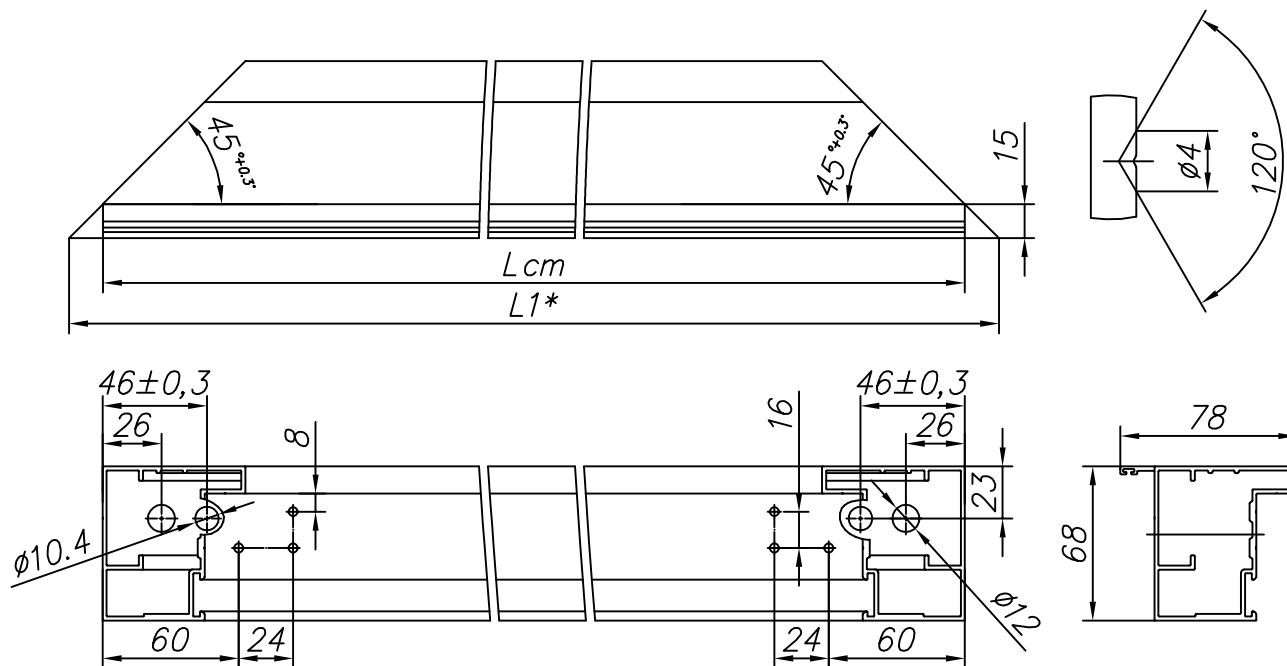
Изготовление стойки из профиля FLGU.400.0108 (для встроенного монтажа)
